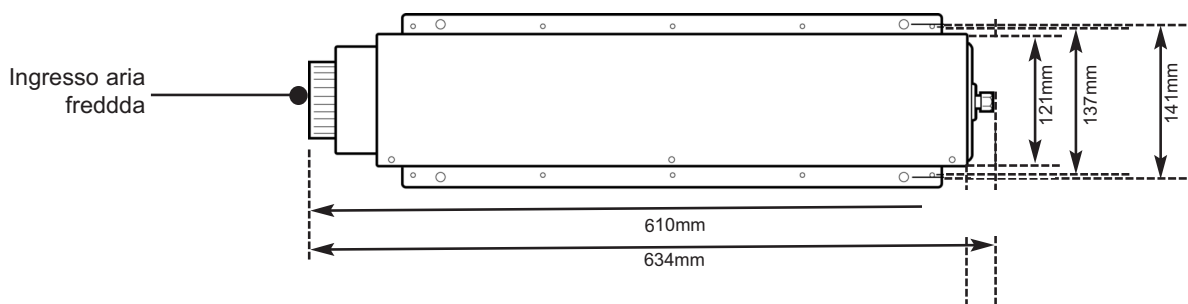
Installazione all'interno – Vista in pianta - SH2201 o SC2201
